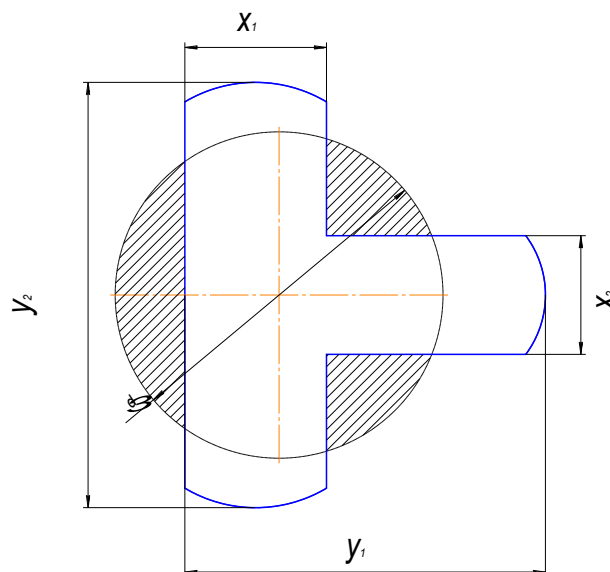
Схема деформации металла таврового профиля из круглой заготовки
